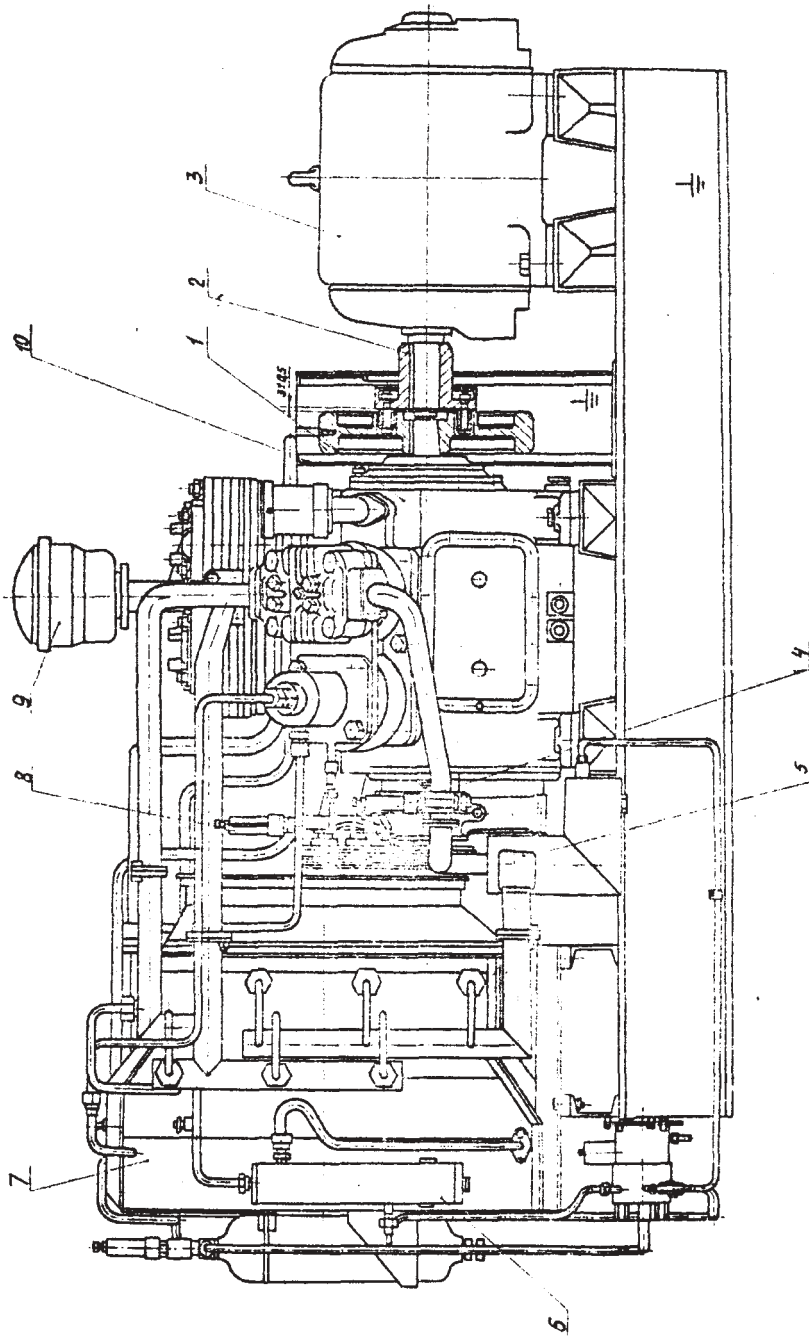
компрессор с приводным двигателем, промежуточной комму-
